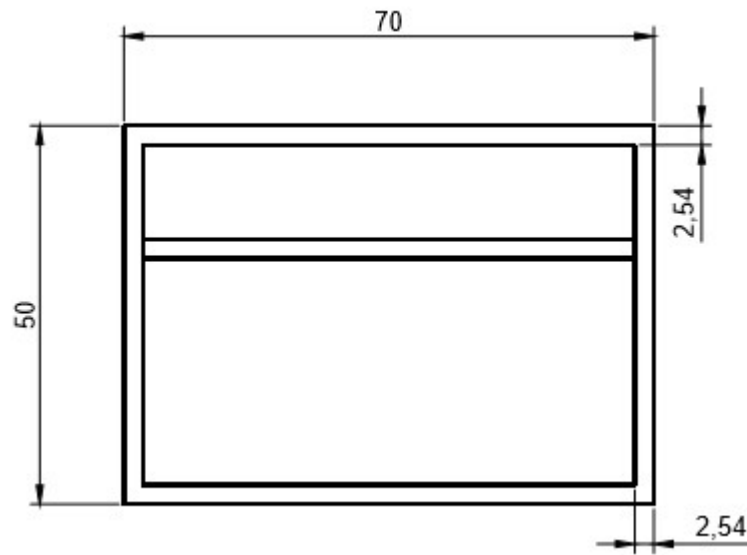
Vista inferior de estructura con dimensiones en centímetros
